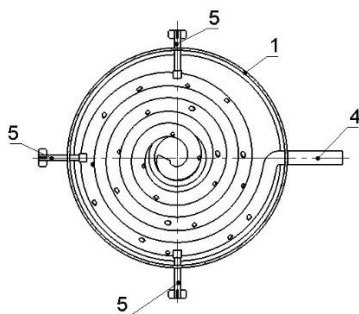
Конструкция пневмосмесителя (вид сверху):
